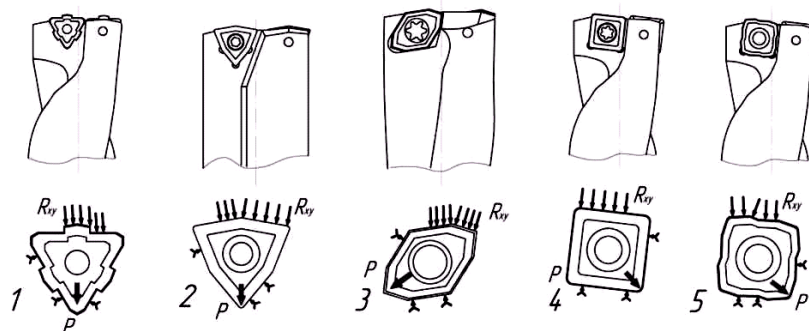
Схемы базирования и крепления центральной режущей пластины сборного сверла фирмы:
